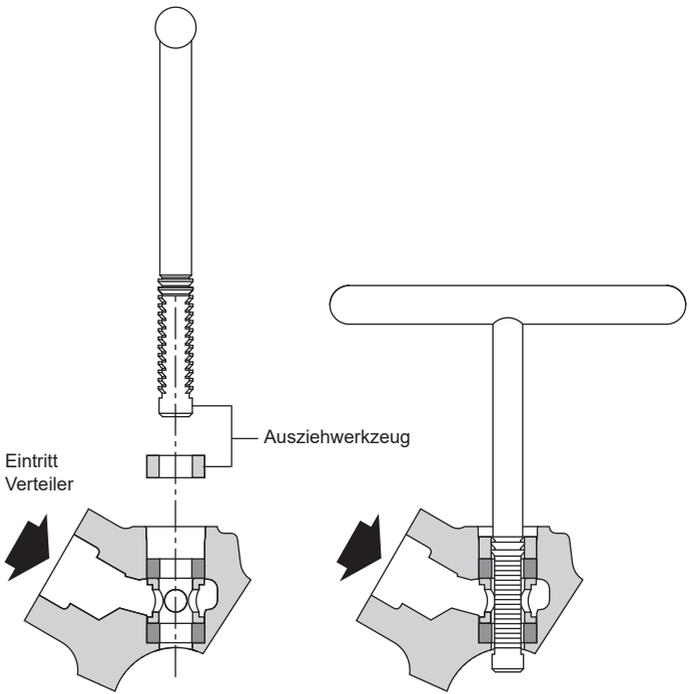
Ausziehwerkzeug für Ventil-Innenteile
